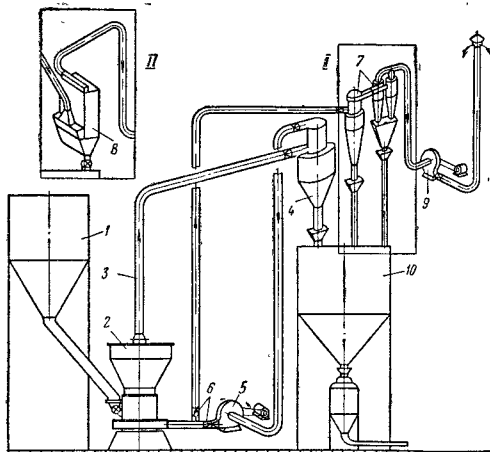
Схема размольной установки с маятниковой мельницей SM-493
